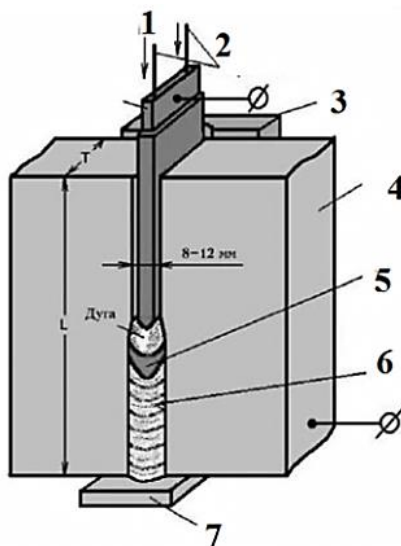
Схема сварки рельс закладным электродом: 1 – изолирующий плавящийся электрод; 2 – присадочные проволоки; 3 – формирующие накладки; 4 – основной металл; 5 – сварочная ванна; 6 – шов; 7 – подкладка
